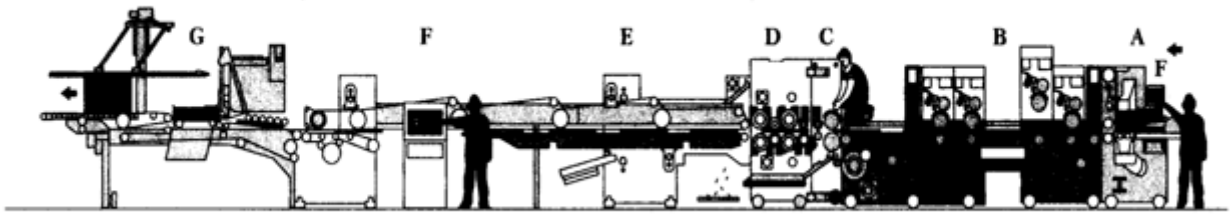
Агрегат фирмы «Мартин» – объединенный в одну линию печатно-высекальный и складывающе-склеивающий агрегат
